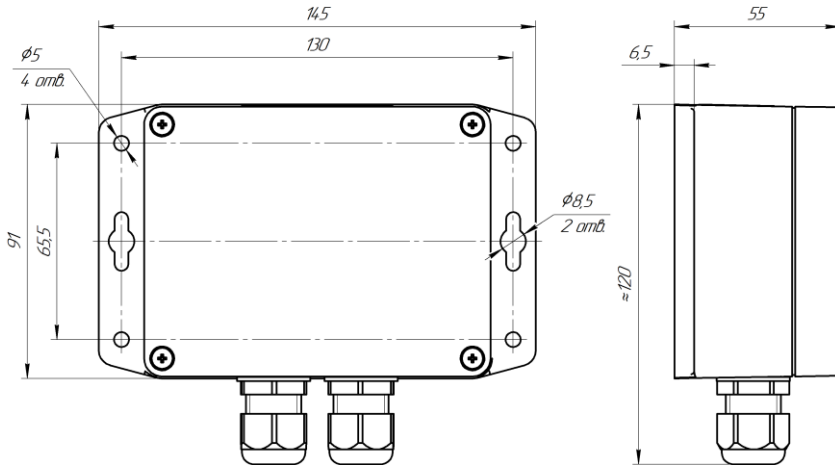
Габаритные размеры и отверстия для монтажа датчика GL-RCM.
